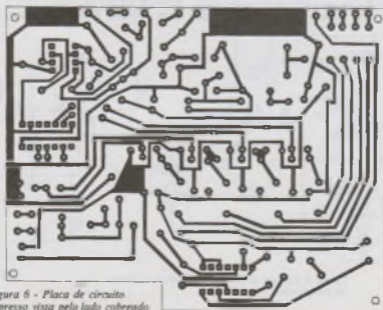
Placa de circuito impresso vista pelo lado cobreado.
